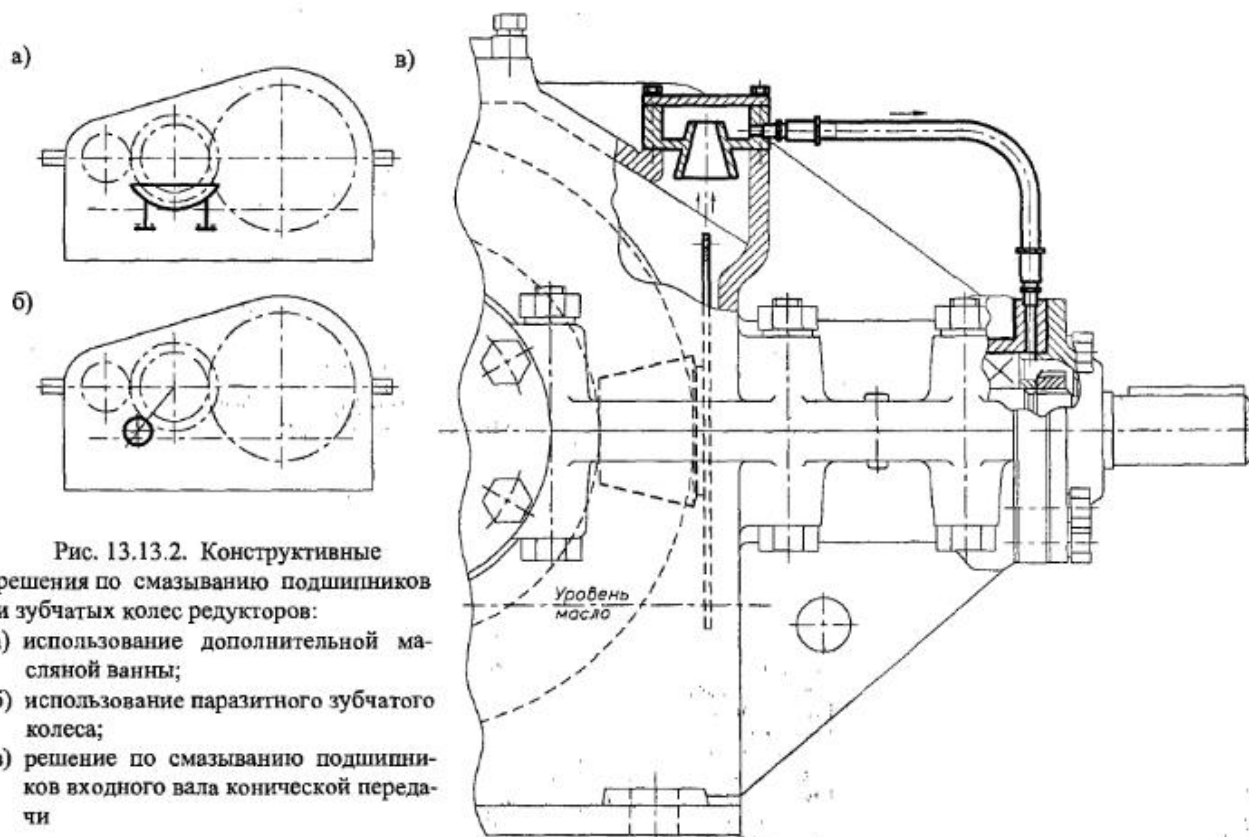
Конструктивные решения по смазыванию подшипников и зубчатых колес редукторов:
